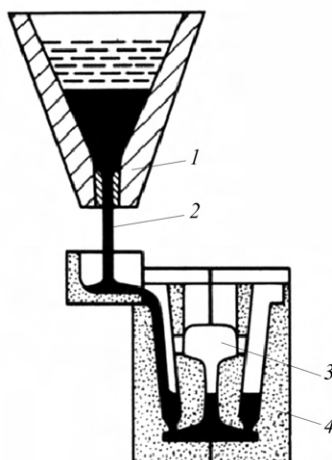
Схема установки для сварки железнодорожных рельсов:
